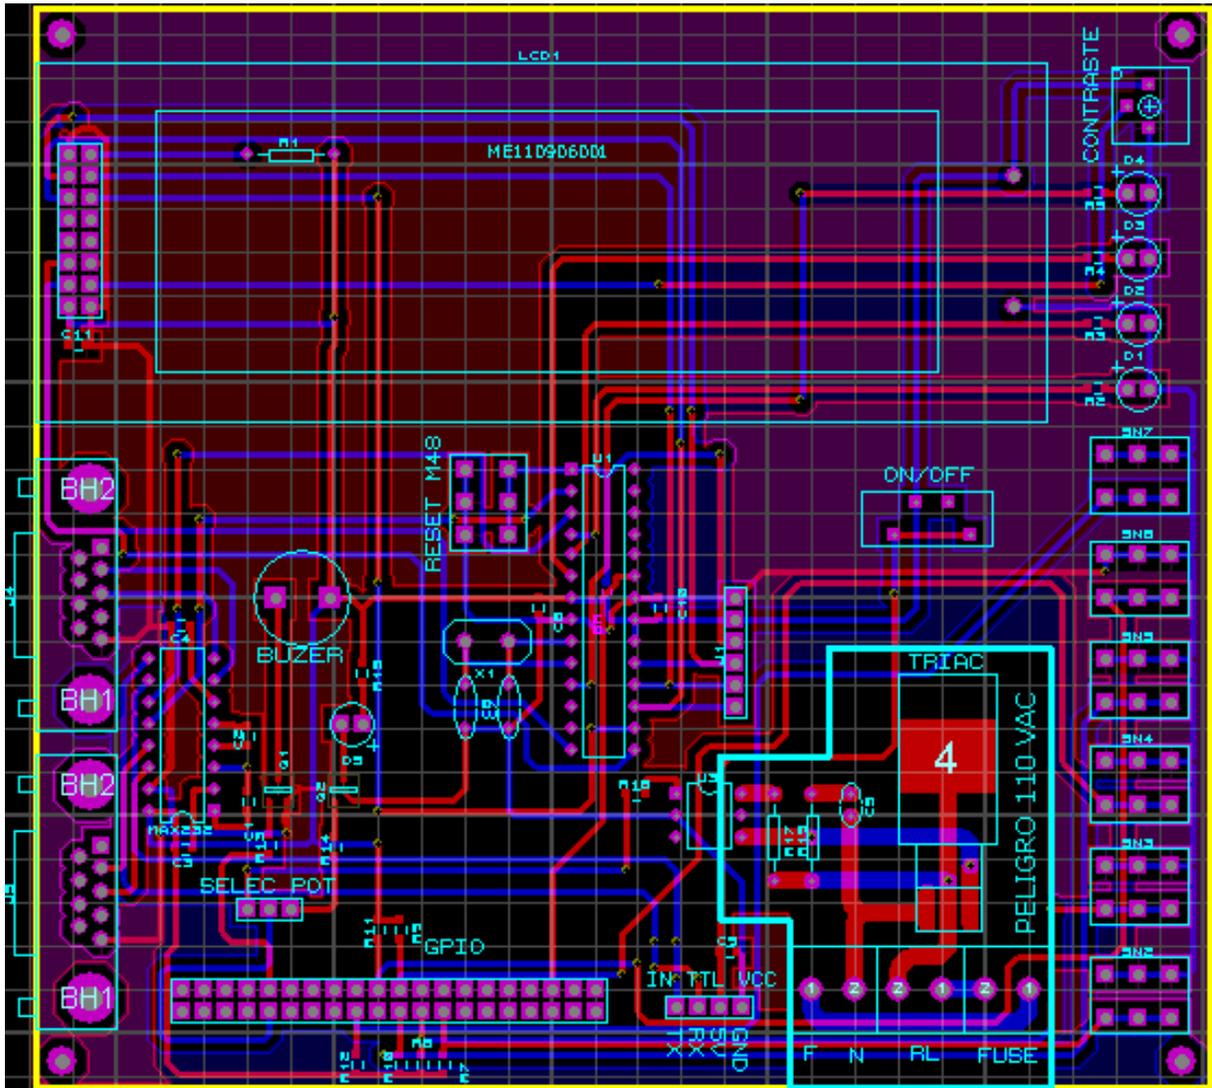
Diseño del PCB de la tarjeta de expansión
